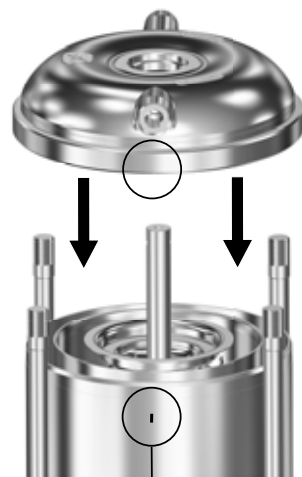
Совмещение крышки головной части (2) и цилиндрического кожуха (55)
